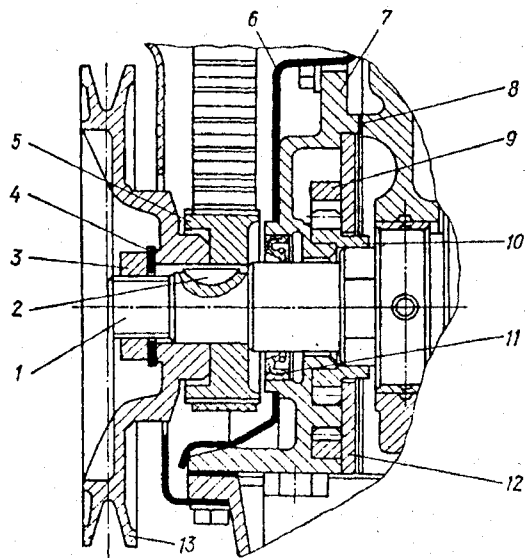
Носок коленчатого вала со шкивом: 1 – вал коленчатый; 2 – шпонка сегментная; 3 – гайка М20х1,5; 4 – шайба; 5 – шкив ведущий коленчатого вала; 6 – внутренний кожух плоскозубчатого ремня; 7 – корпус масляного насоса; 8 – прокладка; 9 и 10 – ведомая и ведущая шестерни масляного насоса; 11 – манжета; 12 – крышка масляного насоса; 13 – шкив привода генератора
